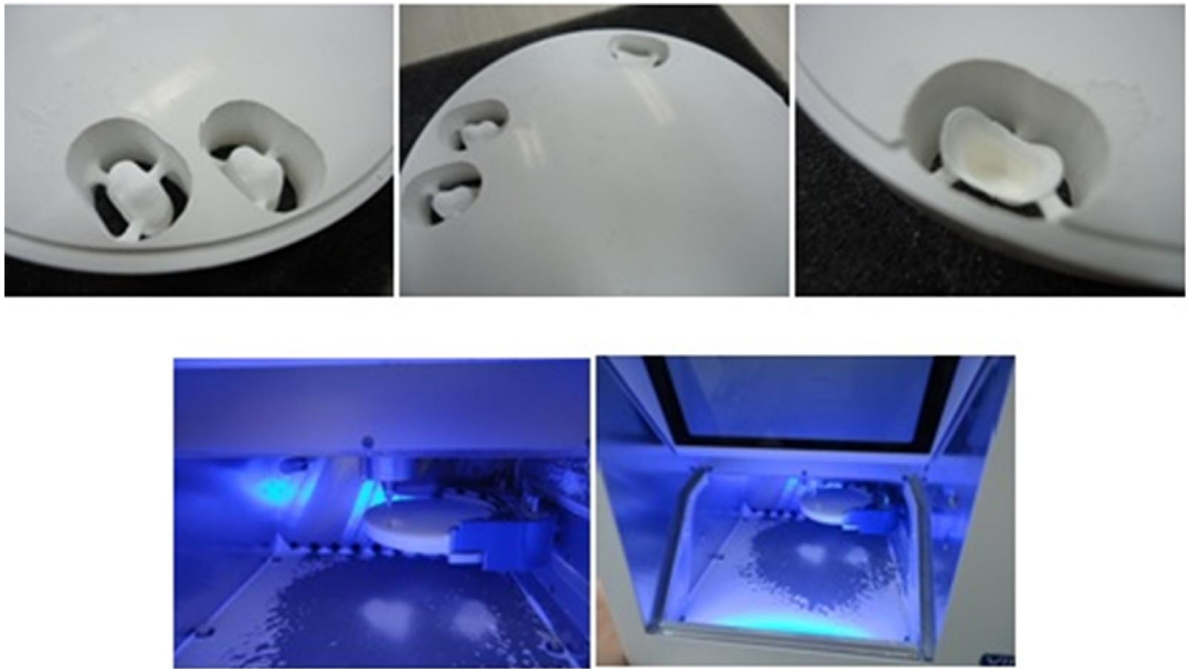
Detalhe dos Blocos pré-sinterizado bicamada de dimensão 98x16mm, em processo de usinagem e casquete usinado.
